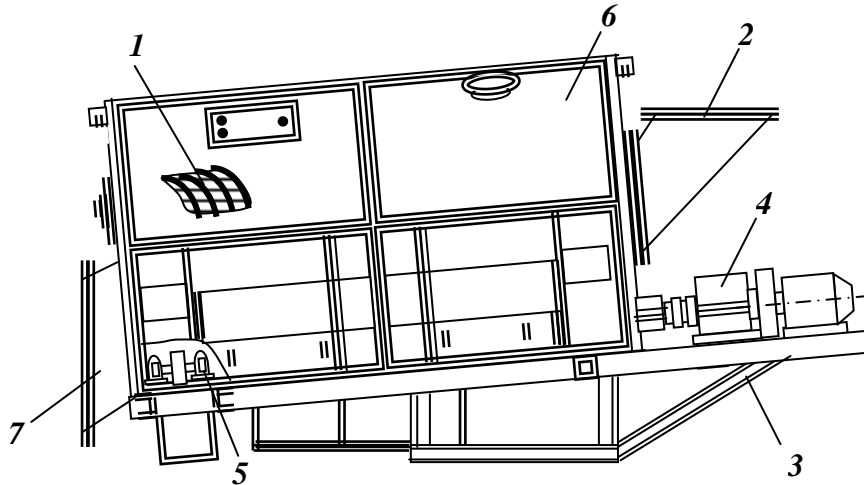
Грохот циліндричний типу ГЦЛ.
